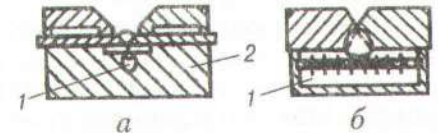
Схеми газових подушок: а, б — одно- і двобічне зварювання; 1 — захисний газ; 2 — мідна підкладка
